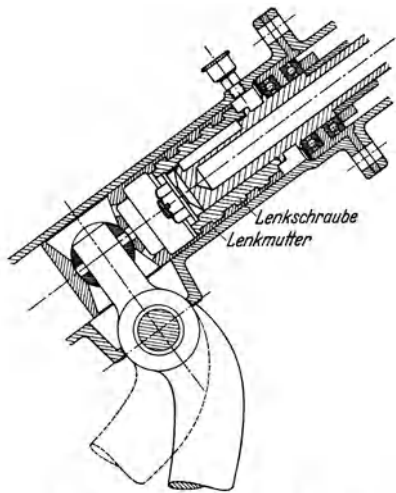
Lenkschraubenge triebe, selbsthemmend.
